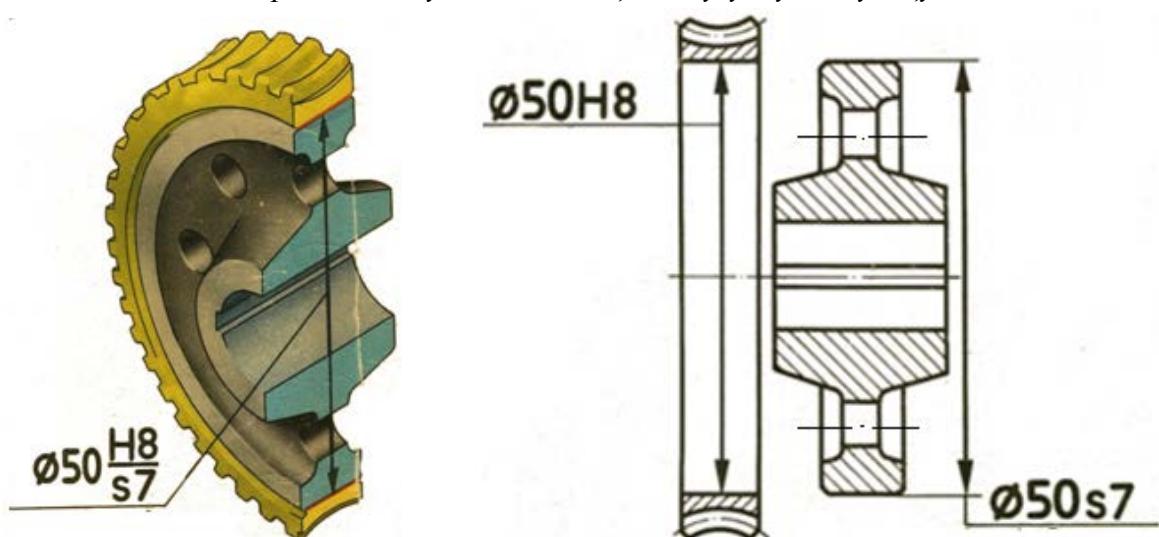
Венец со ступицей червячной шестерни редуктора
